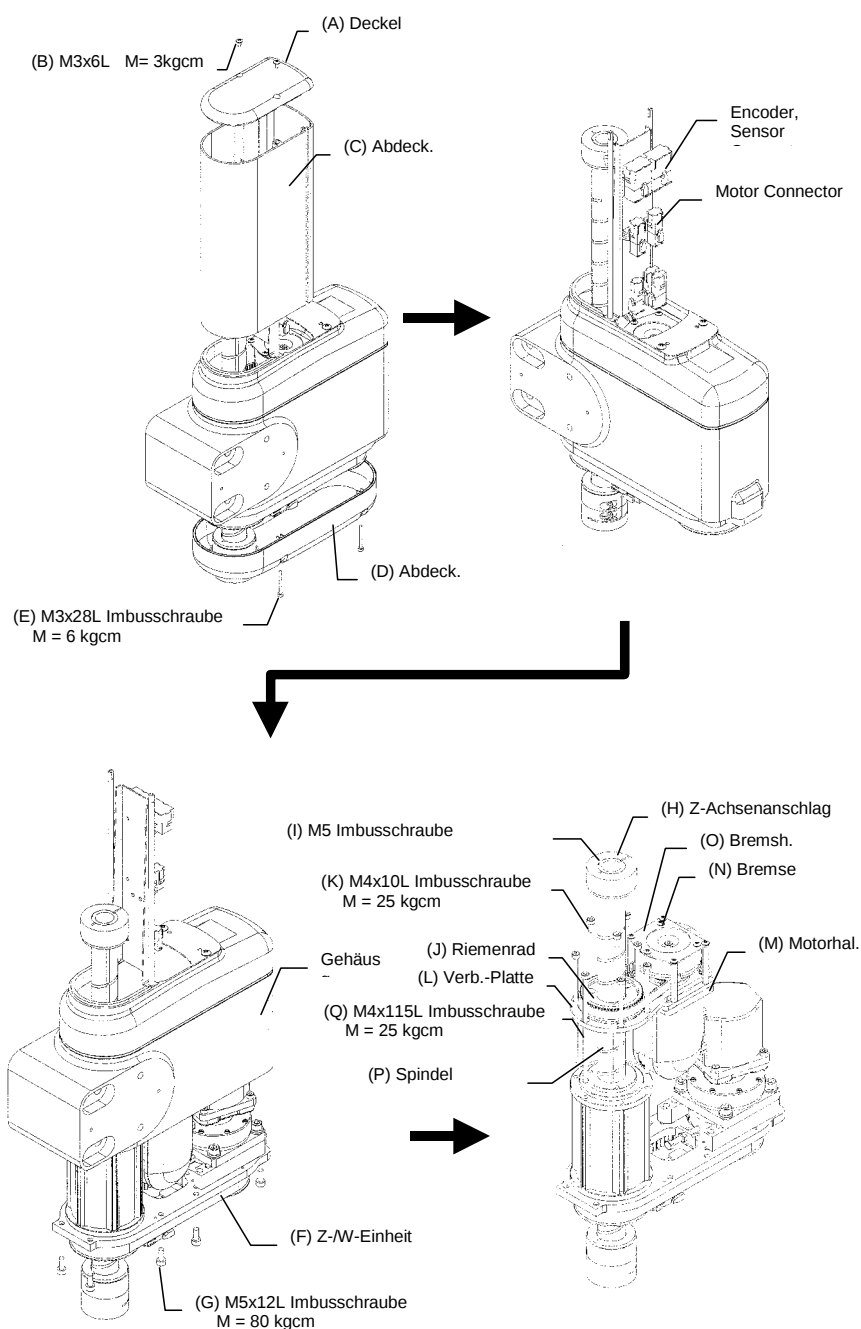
Austausch des Z-Achsenmotors HMZ(W)-S350
